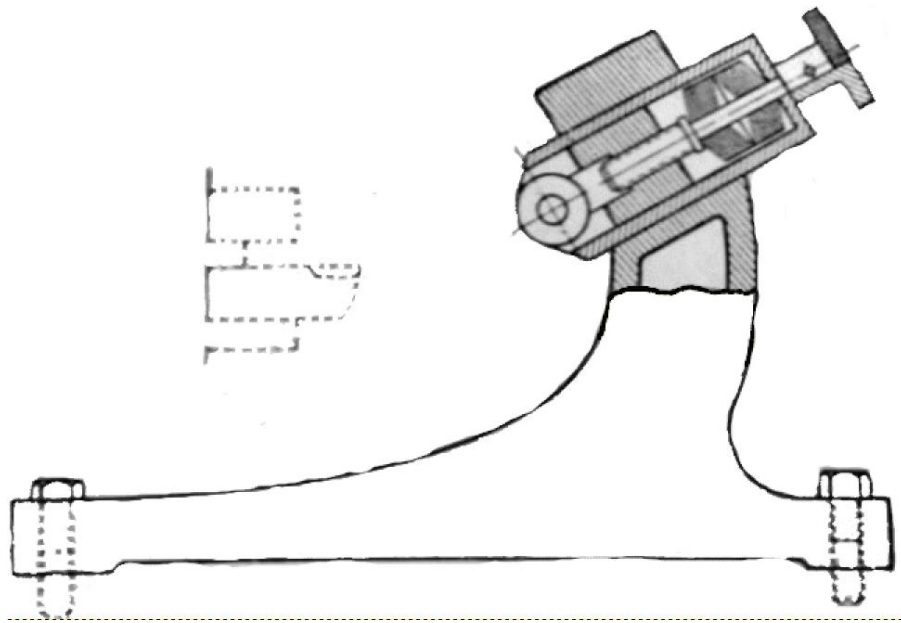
Різець з вібродемпфуючою державкою: 1, 2 і 3 – елементи тримача що мають різну пористість; 4 – різцетримач; 5 – заготовка.
